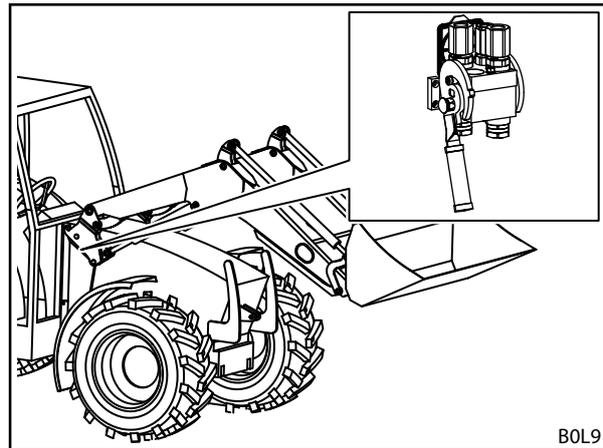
Hydro-Fix: posizione sul caricatore frontale
